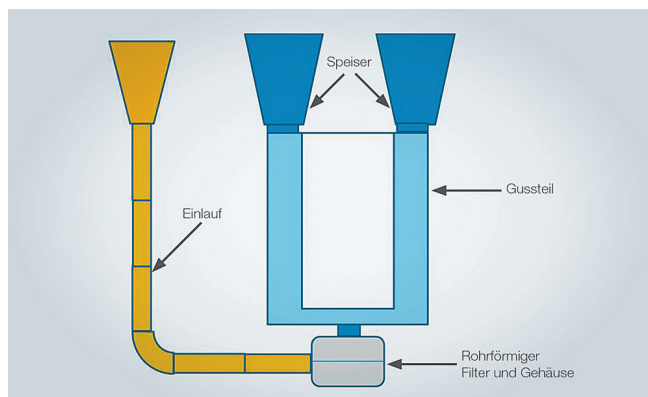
Einbau eines Röhrenfilters mit Gehäuse nahe dem Anschnitt
